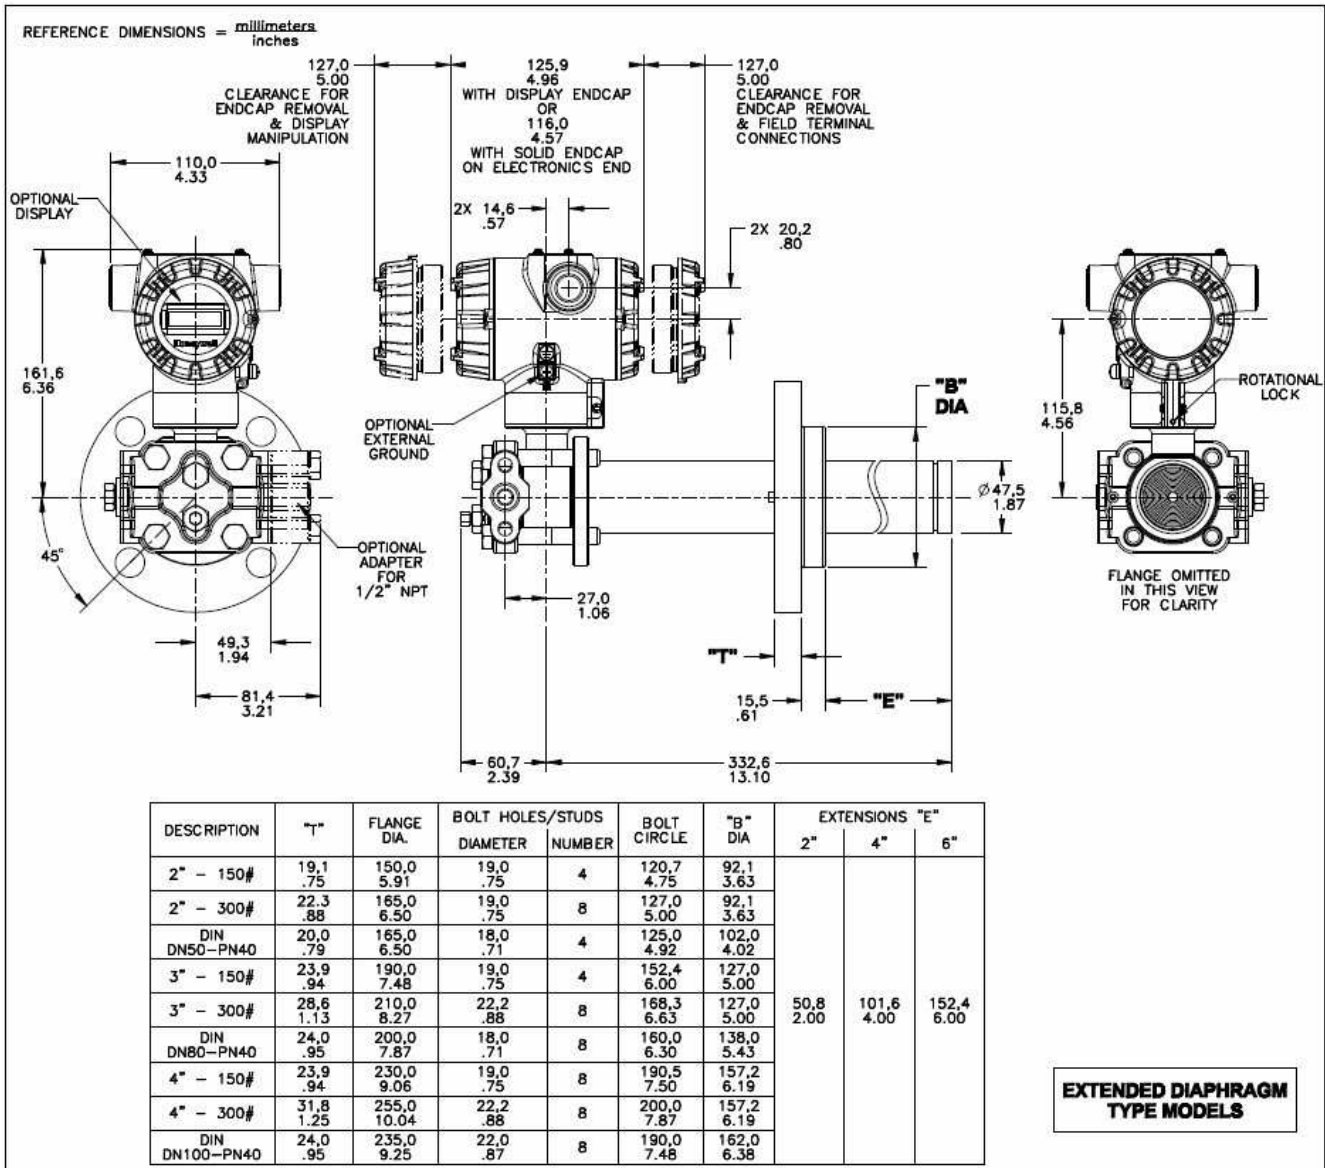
Dimensiunile de montaj pentru traductoare cu extensii de diafragme , modelele STF728 si STF732.
